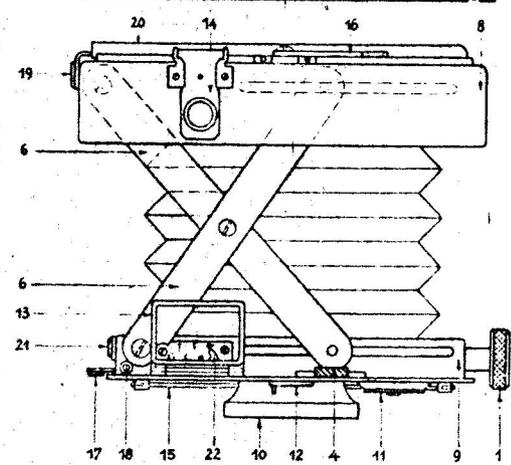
Konstruktionsschema einer Kamera mit verstellbaren Spreizen.
